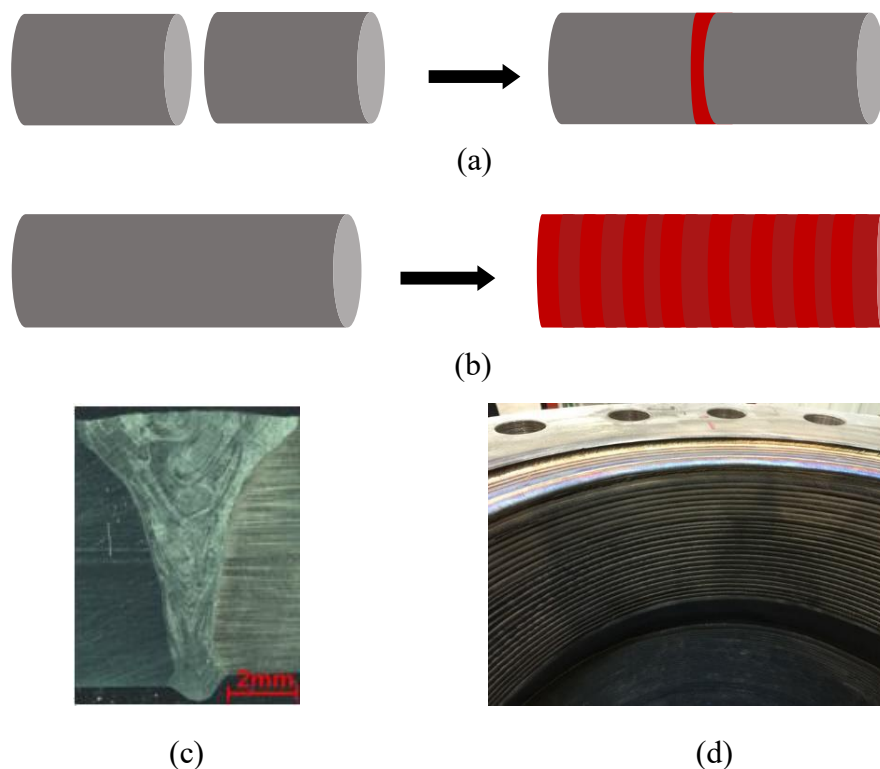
Representação esquemática de soldagem de união (a) e de soldagem de revestimento (b), exemplo real da soldagem de união (c) e aplicação do revestimento a região interna de tubos na indústria de óleo e gás (d).
